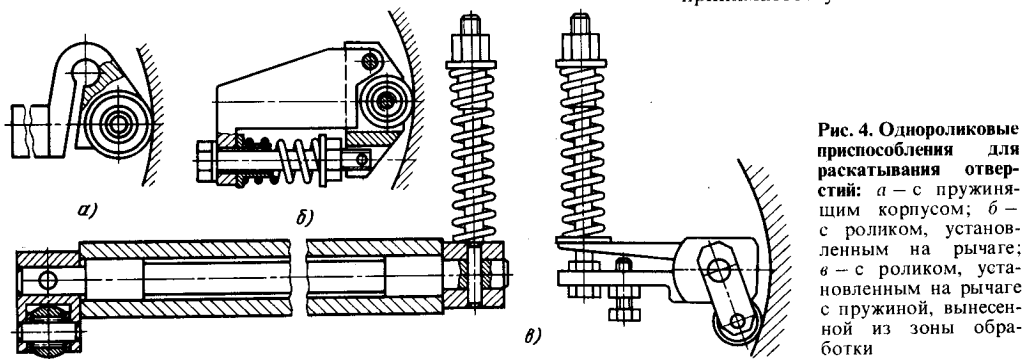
Однороликовые приспособления для раскатывания отверстий: а — с пружиной-корпусом; б — с роликом, установленным на рычаге; в — с роликом, установленным на рычаге с пружиной, вынесенной из зоны обработки
